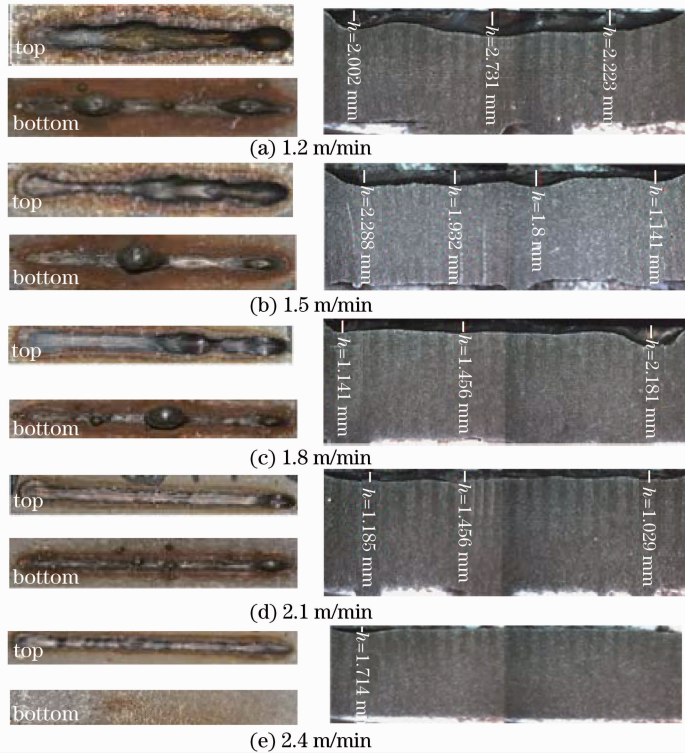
不同焊接速度时焊缝上下表面(左列)及纵截面(右列)
